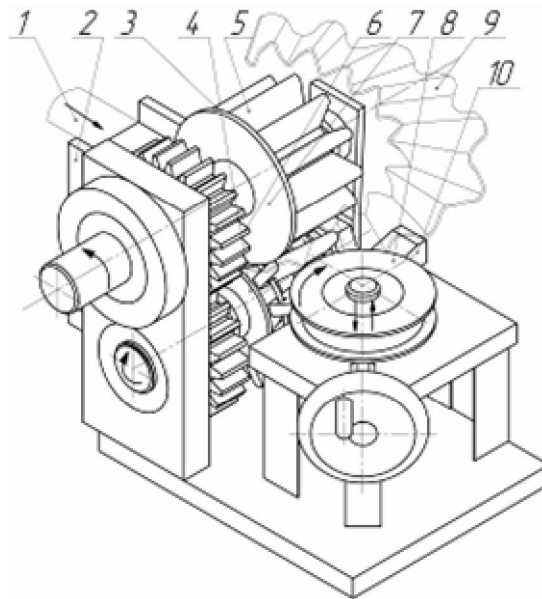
Пристрій для виготовлення ГГЗ способом прокатування і завивання
